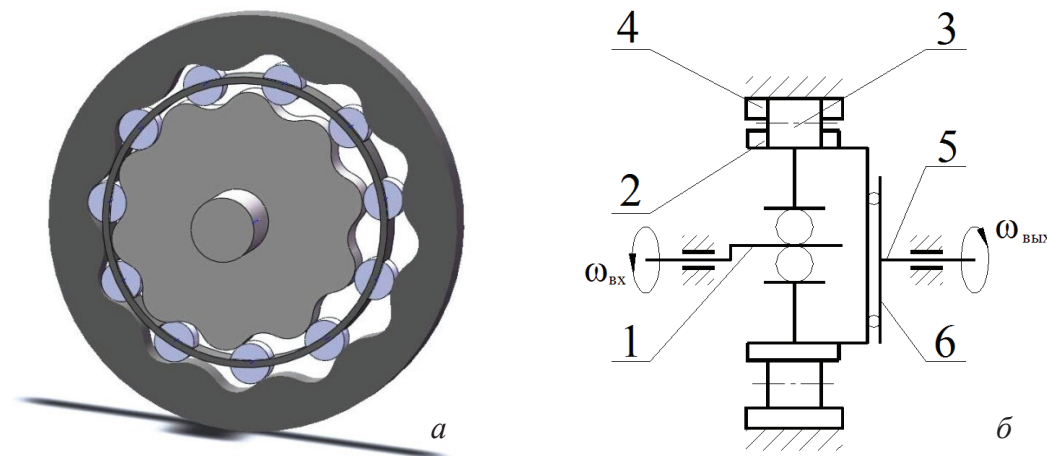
Передача с промежуточными телами качения и свободной обоймой: а) общий вид; б) кинематическая схема
